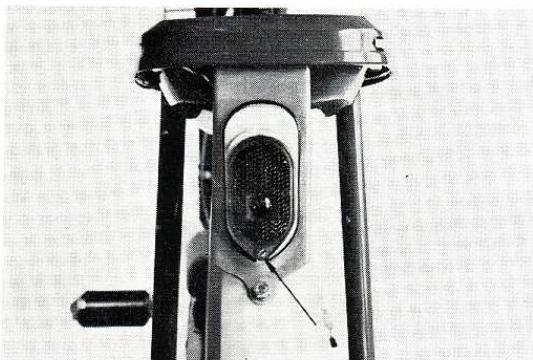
DÉMONTAGE DU FEU ARRIÈRE.
